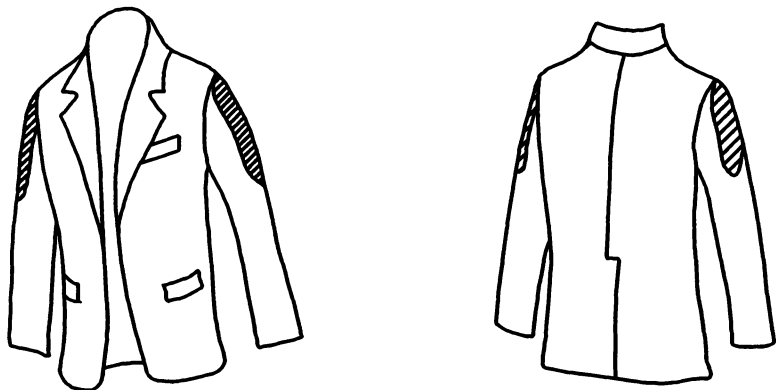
Схема расположения обрабатываемых участков верха рукавов
